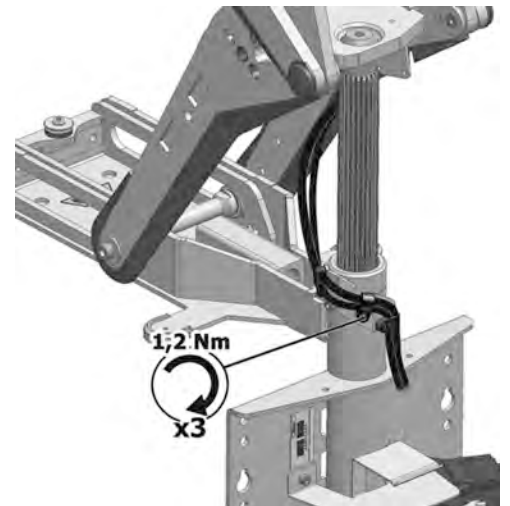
Das Kabel ist mit drei Kabelhalterungen an der Säule befestigt und jeweils mit einer Schraube montiert.
